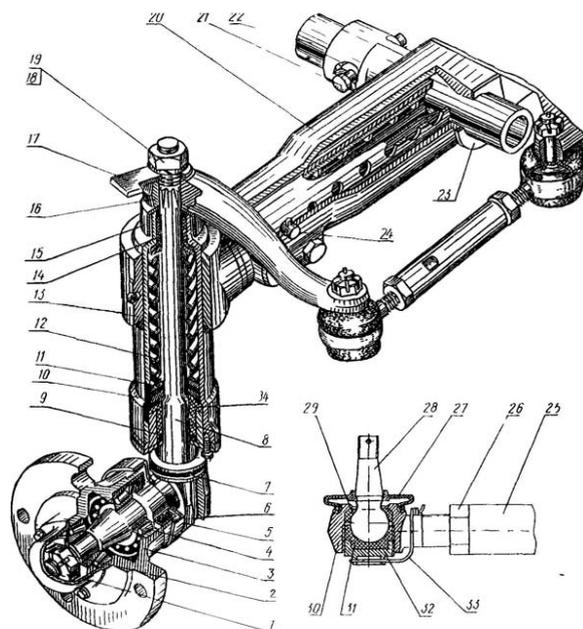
Передняя ось трактора. 1 — колпак; 2 — гайка; 3 — ступица; 4 — роликподшипник; 5 — защитная обойма; 6 — уплотнительная манжета; 7 — тарельчатые пружины; 8 — левая поворотная цапфа; 9 — нижнее уплотнение; 10, 23 — шайбы; 11 — шарикоподшипник; 12 — пружина; 13 — выдвигной кулак; 14, 34 — втулки; 15 — защитный кожух; 16 — поворотный рычаг; 17 — кронштейн крыла; 18, 19 — гайка, пружинная шайба; 20 — трубчатая балка; 21, 24 — пальцы; 22 — ось качения; 25 — труба рулевой тяги; 26 — контргайка; 27 — защитный чехол; 28 — шаровой палец; 29 — вкладыш верхней; 30 — наконечник рулевой тяги; 31 — вкладыш нижней; 32 — пробка регулировочная; 33 — контровочная проволока.
